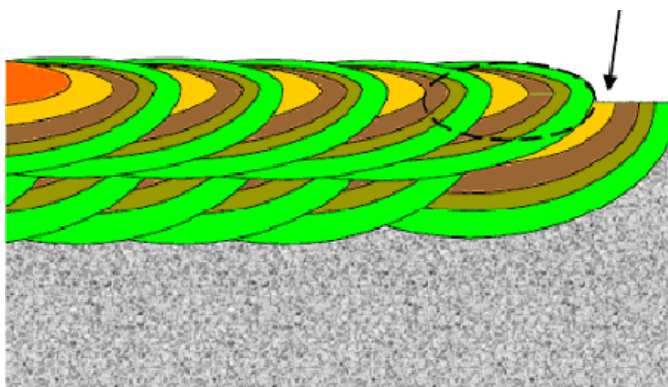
Efeito da aplicação da segunda camada do metal de solda e na ZTA da primeira camada – Exploring temper bead Welding (Walter J. Sperko – Welding Journal – July – 2005).
